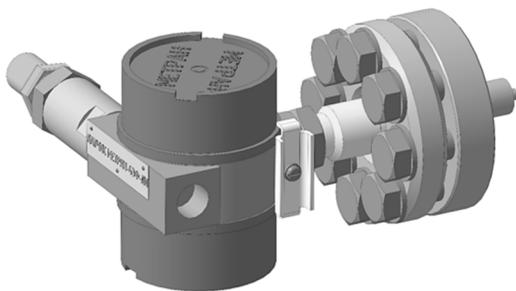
3D-модель датчика избыточного давления Метран-43ДИ
